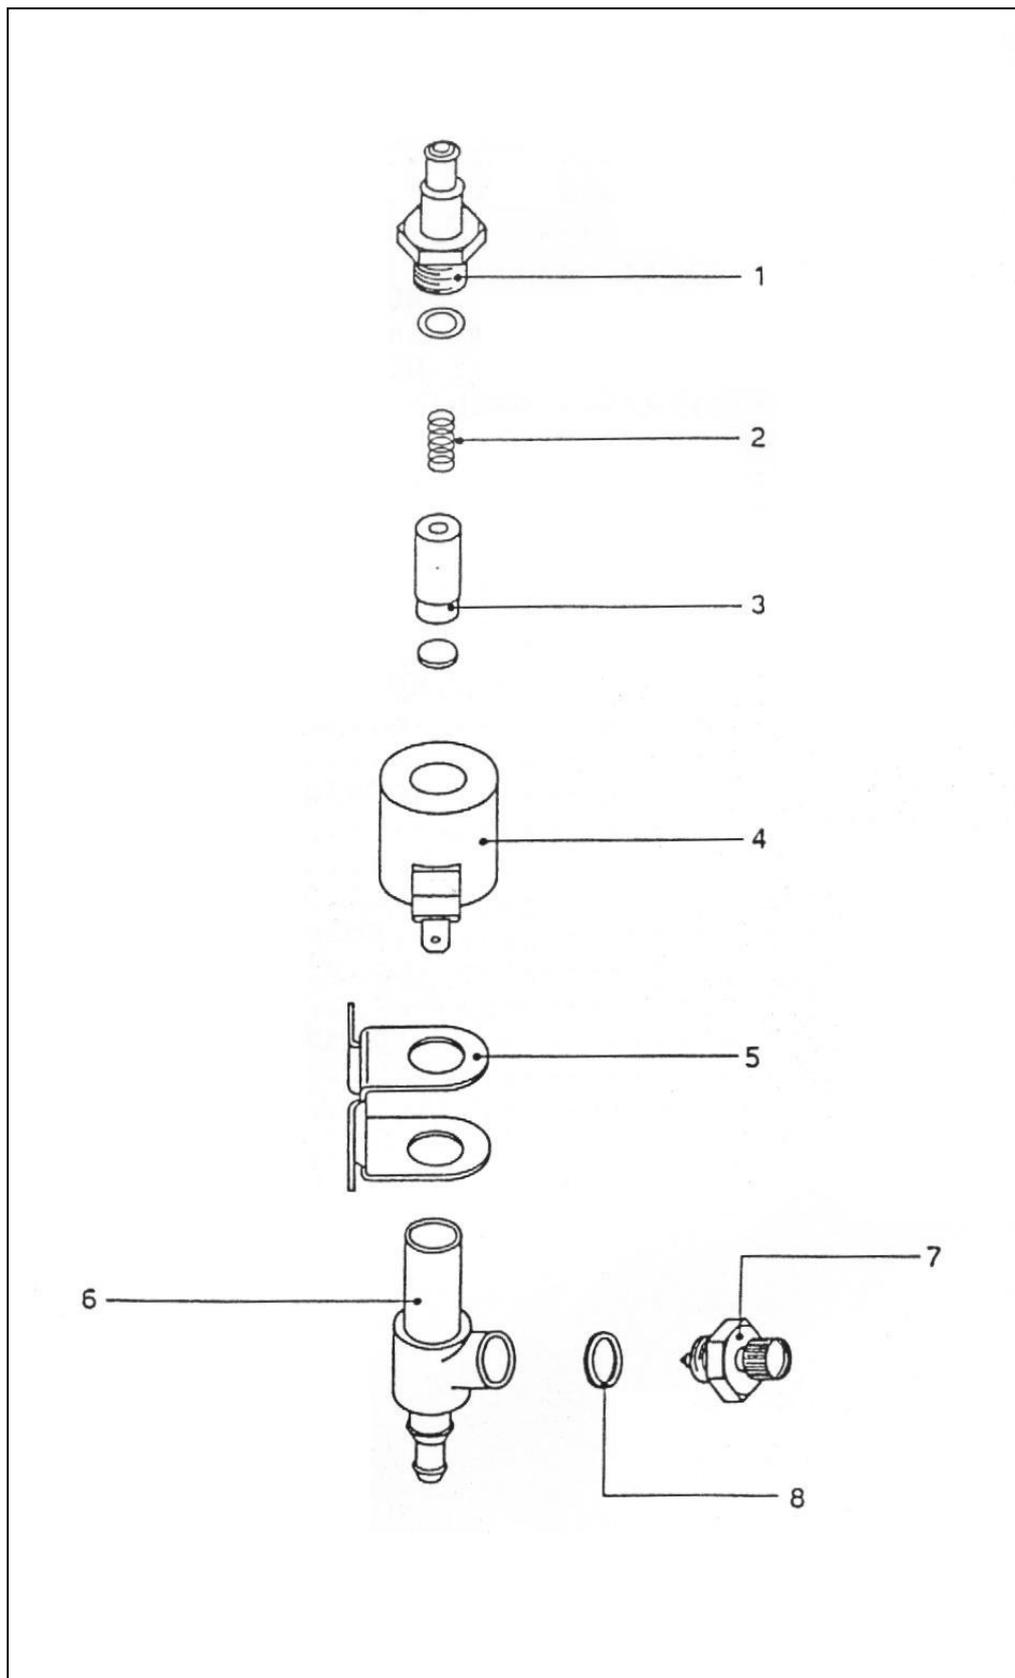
Esquema del despiece de la Electroválvula Gasolina
